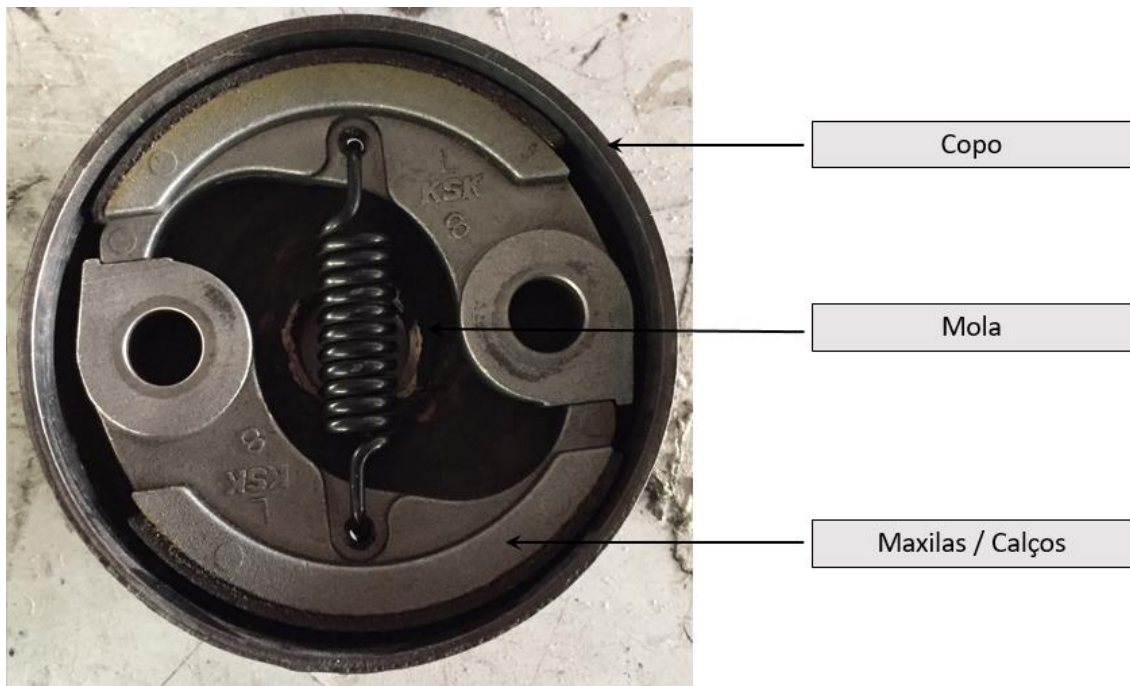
Conjunto de embraiagem centrífuga pertencente ao motor Honda GX35.
